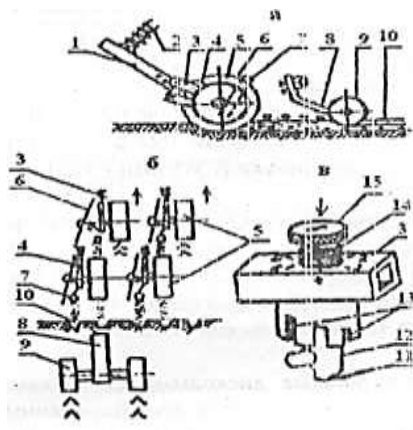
Однодисковая сошниковая группа к сеялке СЗ-5,4: а, б – схема работы сошников; в – регулятор глубины: 1 – поводок; 2 – пружина; 3 – корпус сошника; 4 – регулятор; 5 – опорно-прикатывающий каточек; 6 – диск; 7 – направитель семян; 8 – пружинный поводок; 9 – прикатывающий каточек; 10 – семена; 11 – хвостовик; 12 – штифт; 13 – прорезь; 14 – пружина; 15 – головка-указатель
